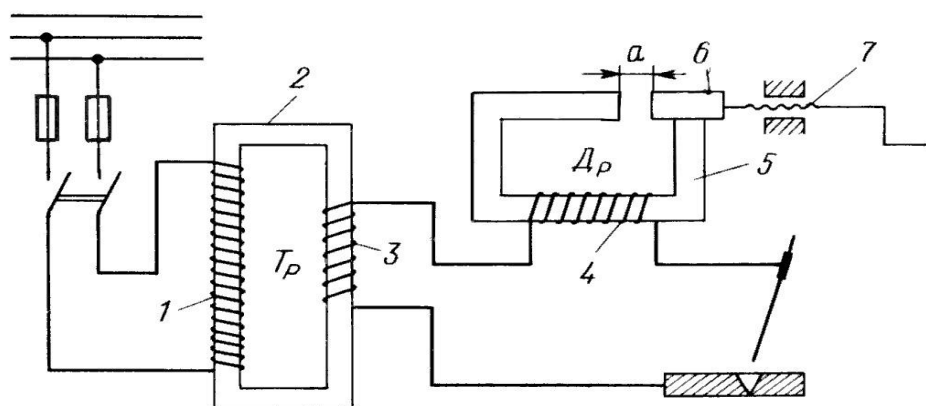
Схема сварочного аппарата с отдельным дросселем
